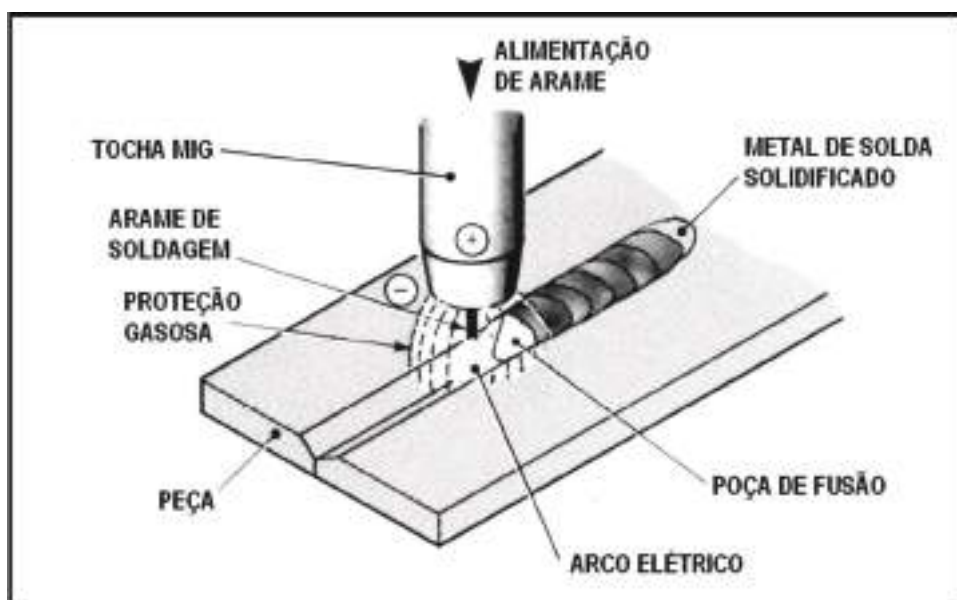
Processo básico de soldadura MIG/MAG.
